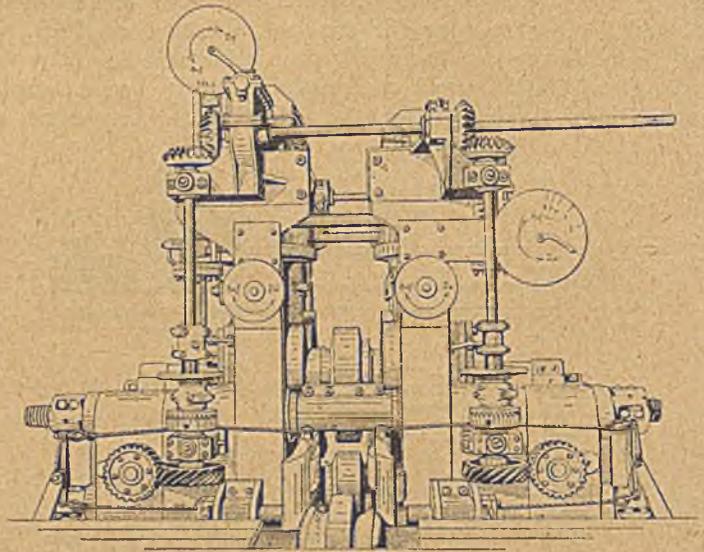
Universalvorgerüst mit vier anstellbaren Walzen (Vorderansicht).
